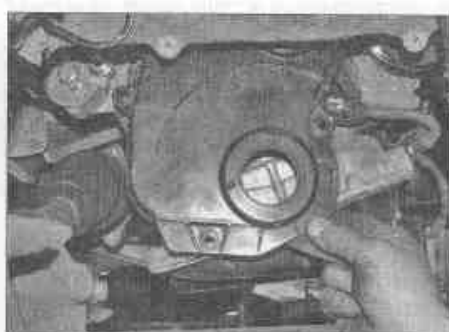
,в. ...затем выверните болты и снимите нижнюю крышку ремня газораспределительного механизма с блока цилиндров
